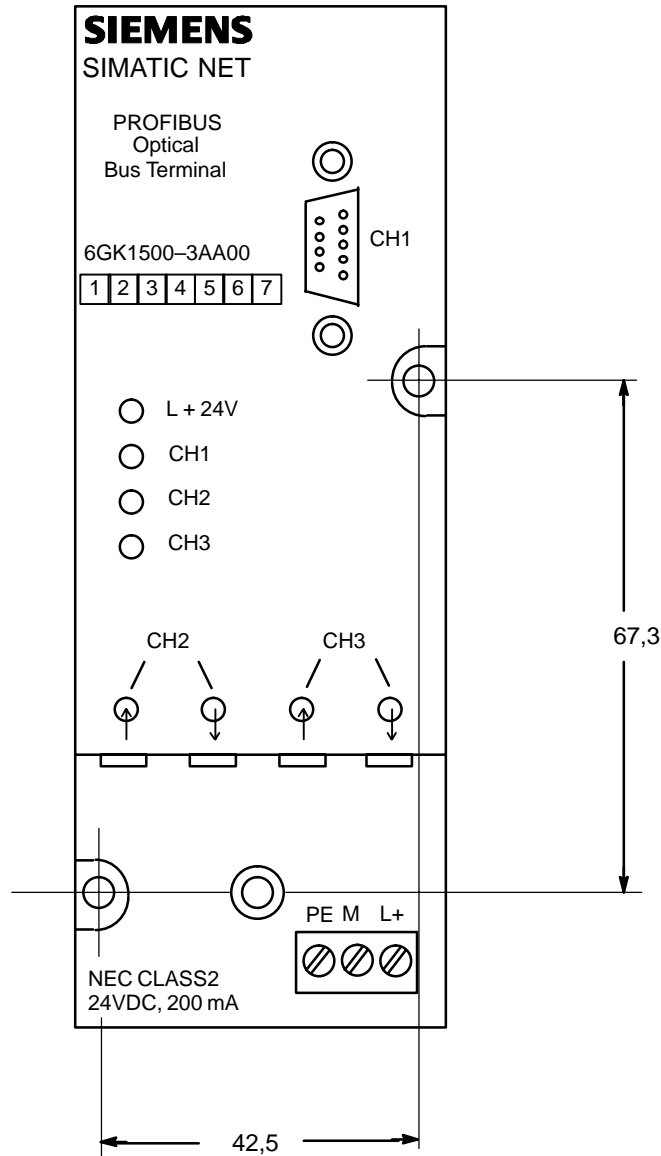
Montage eines Moduls auf einer Montageplatte
